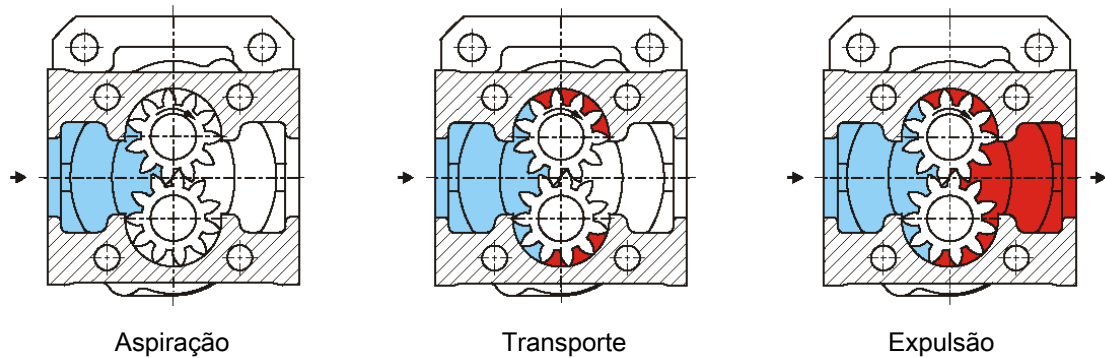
Princípio de bombeamento da bomba de engrenagens
